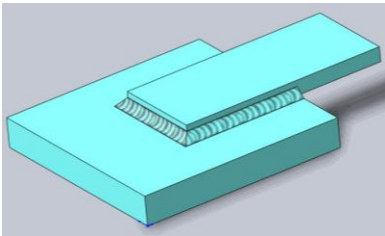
Готова деталь зі зварним напускним з'єднанням
